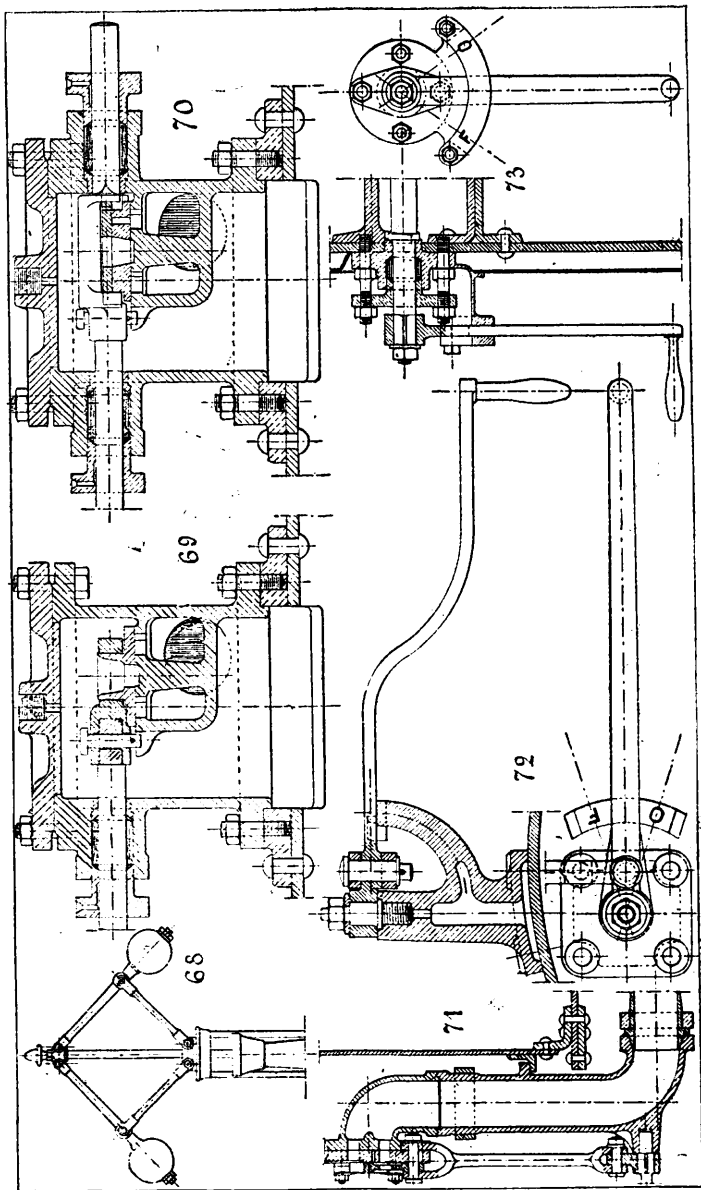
Régulateur à boules. — Fig. 69. Régulateur de locomotive, à un tiroir. — Fig. 70. Régulateur à deux tiroirs. — Fig. 71. Régulateur dans le dôme. — Fig. 72. Levier de manœuvre du régulateur Crampton. — Fig. 73. Levier de manœuvre du régulateur dans le dôme.
